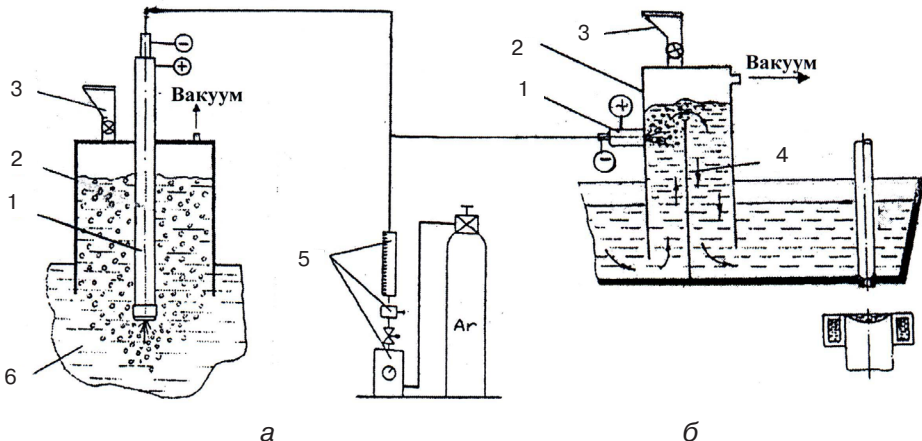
Схемы вакуумно-плазменной обработки сплавов в ковше (а) и при непрерывной разливке металла (б): 1 – плазмотрон; 2 – камера вакуумная; 3 – дозатор для реагентов; 4 – перегородка; 5 – система подвода газа к плазмотрону; 6 – расплав
